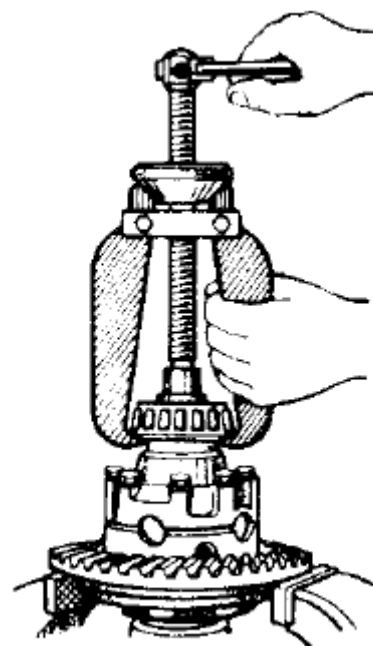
Снятие внутреннего кольца подшипника дифференциала
